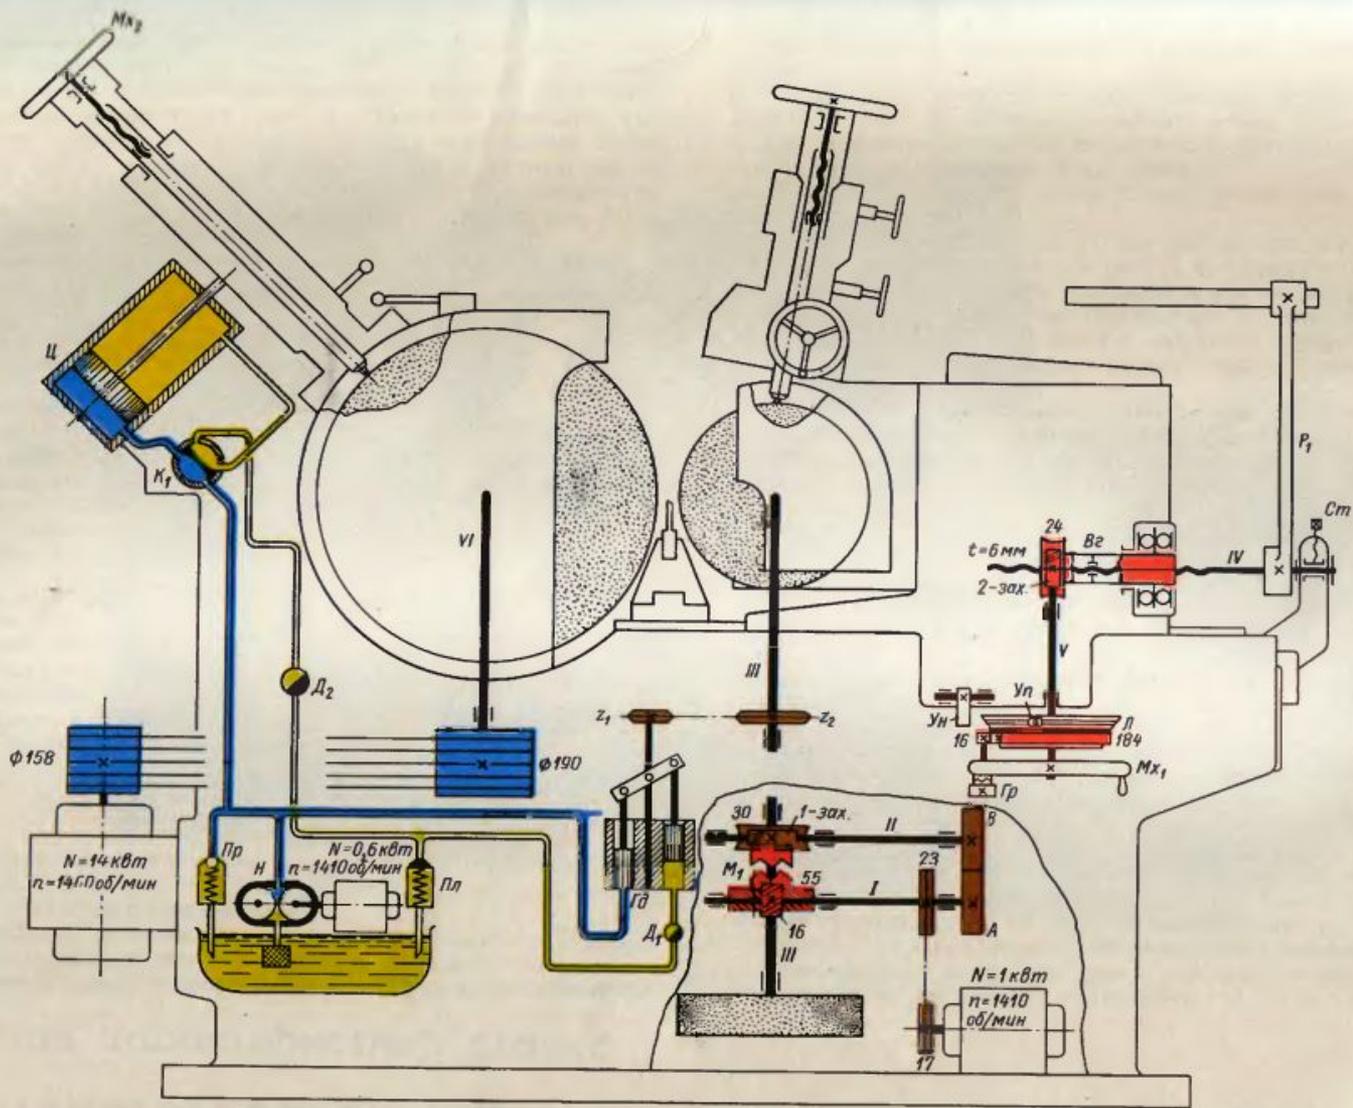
Кинематическая схема бесцентрового круглошлифовального станка модели 3180
